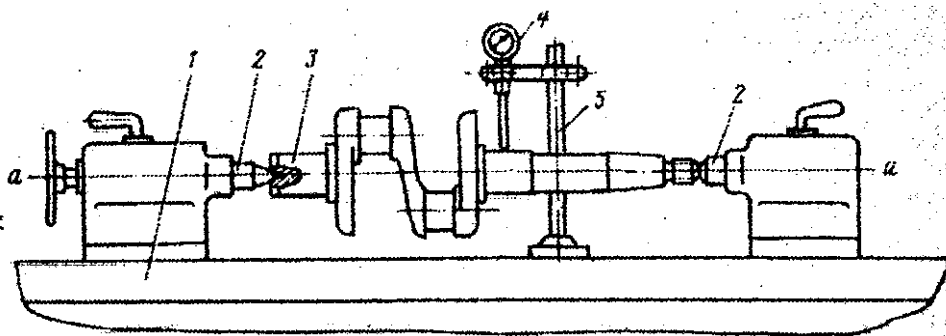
Пристрій для перевірки колінчатого вала компресора
